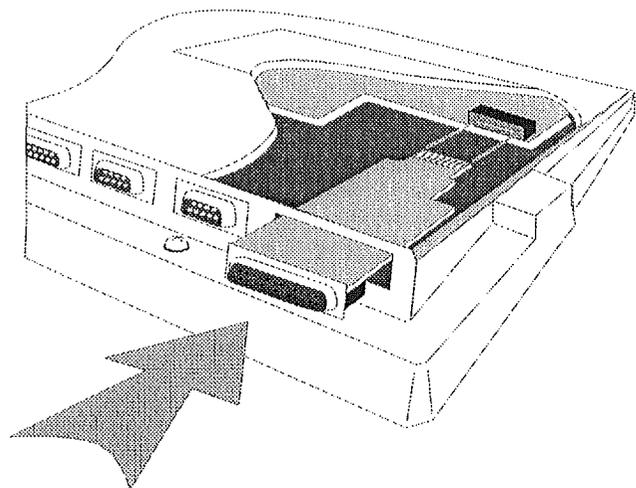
Aligner les connecteurs et pousser pour insérer
